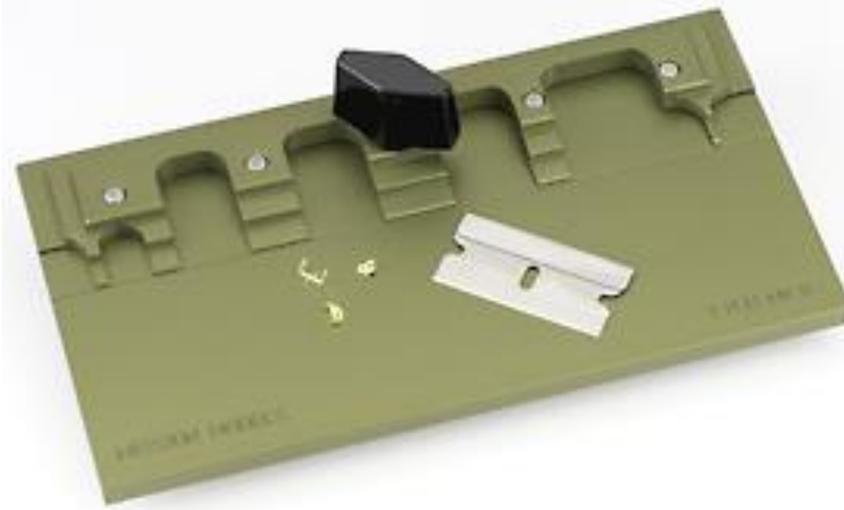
Mecanismo con la cabeza de doblado desensamblada.
